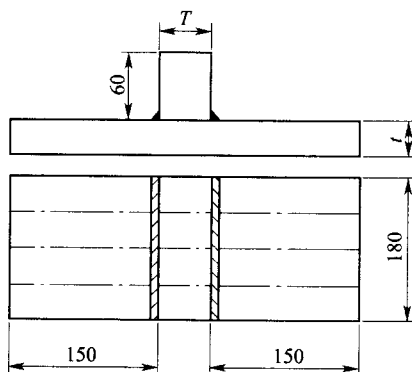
T形接头角焊缝试板的形状和尺寸
